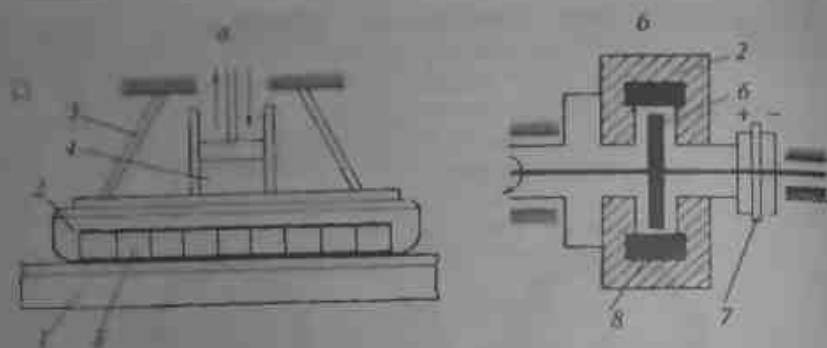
Магнито-рельсовый тормоз (а) и порошковая муфта (б): 1 — рельс, 2 — соленоид, 3 — баушка, 4 — прижимной цилиндр, 5 — пружины, 6 — ротор, 7 — плита давления, 8 — обмотка (по Чичинадзе и Брауну)
